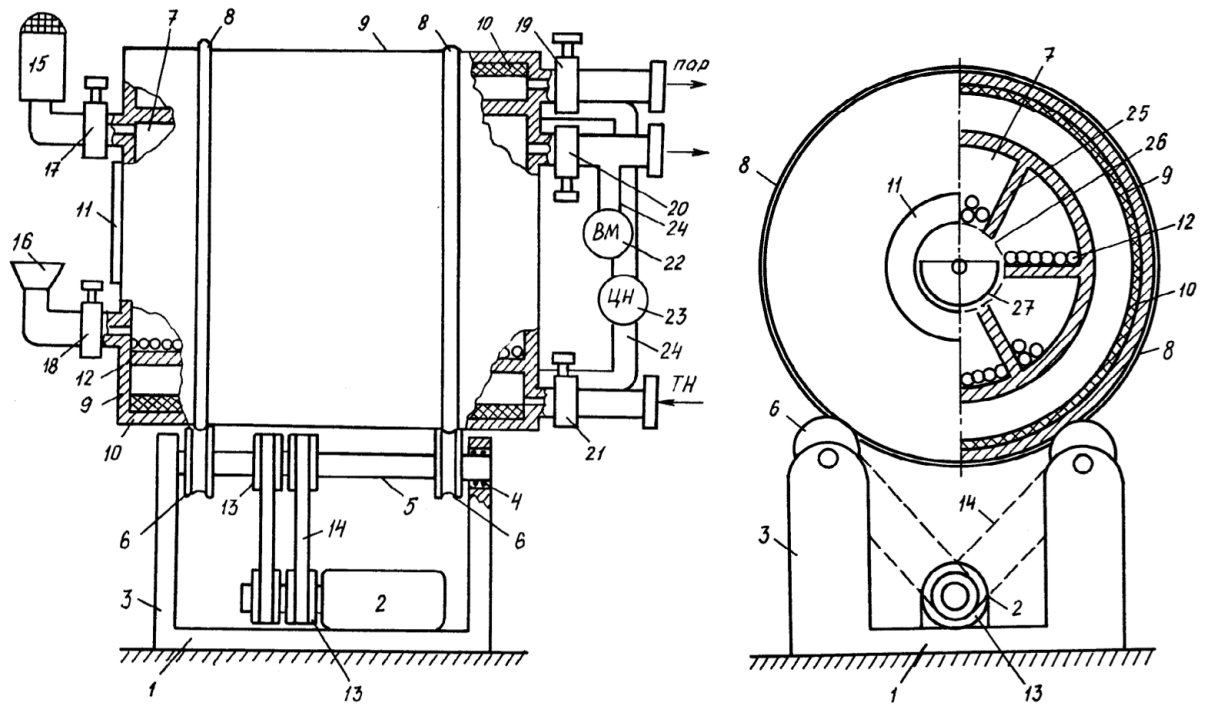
Устройство вакуумной сушки жидких продуктов: 1 – станина; 2 – силовой двигатель; 3 – боковая станина; 4 – подшипник; 5 – вал; 6 – ролик опоры; 7 – вакуумная сушильная камера; 8 – кольцевая направляющая; 9 – тепловая рубашка; 10 – теплоизоляция рубашки; 11 – разгрузочная дверца; 12 – мелющие тела; 13 – блок привода; 14 – приводной ремень; 15 – воздушный фильтр; 16 – загрузочная воронка; 17÷21 – вентили; 22 – вакуумметр; 23 – циркуляционный насос; 24 – наружная труба; 25 – полка; 26 – цилиндрическое сито; 27 – сборник готового продукта
